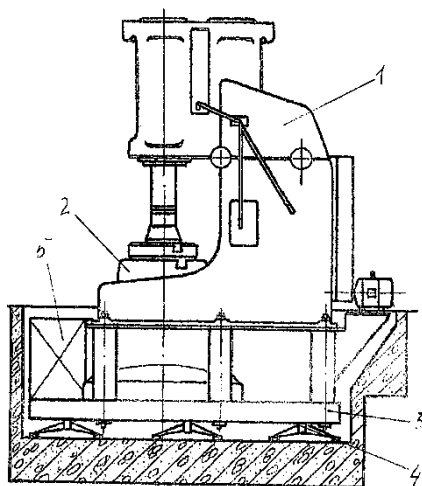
Виброизолирующая установка пневматического ковочного молота:
